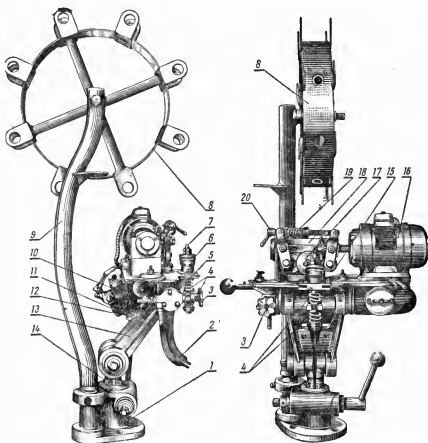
Наплавочная головка с электромагнитным вибратором:
